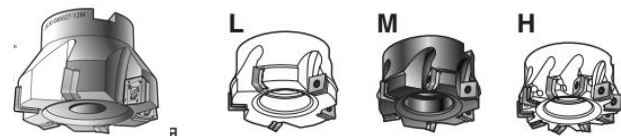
Загальний вигляд і оброблювальні поверхні торцenasадних фрез типу HoliDo [5]
